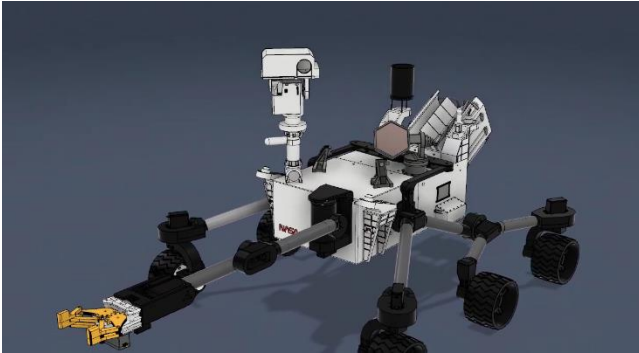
Diseño de prototipo en Solidworks del robot explorador para entornos peligrosos.
